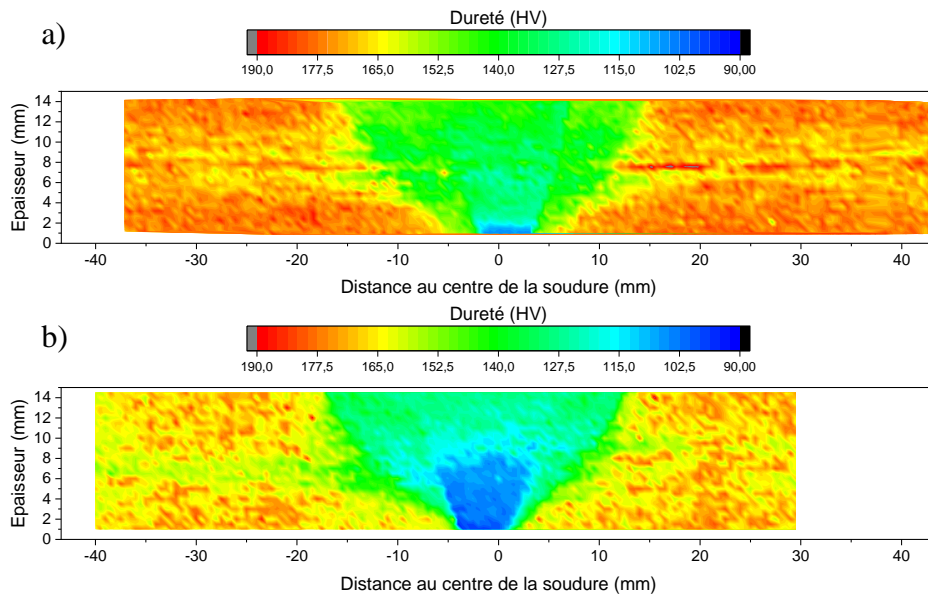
Cartographie de dureté après le traitement thermique a) pour la condition de soudage numéro 1, b) pour la condition de soudage numéro 2
